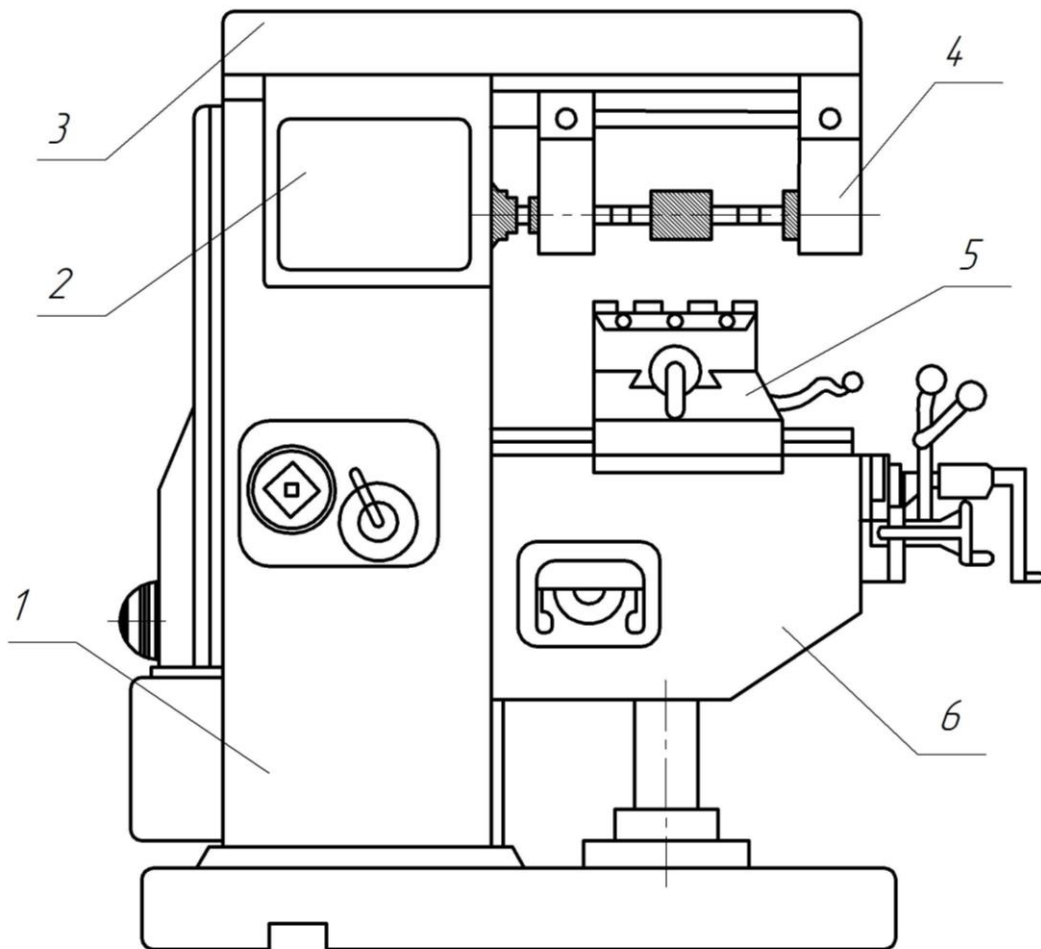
Загальний вигляд горизонтально-фрезерного верстата
